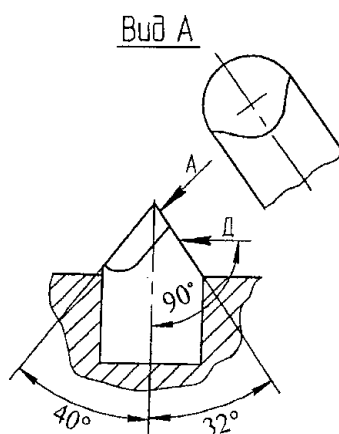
Копытообразный зубок, закрепленный в теле шарошки.
